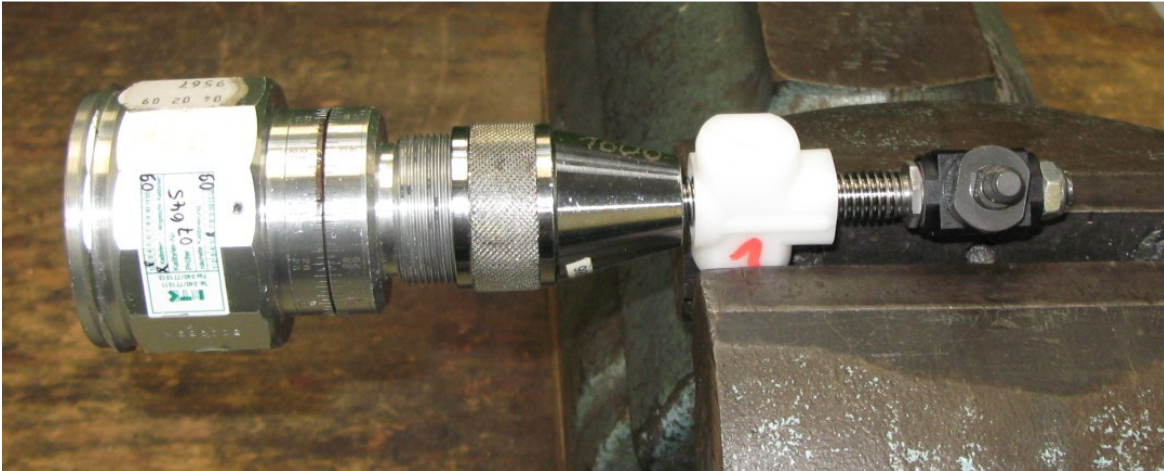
Messaufbau Gewinde Spindelmutter HV
